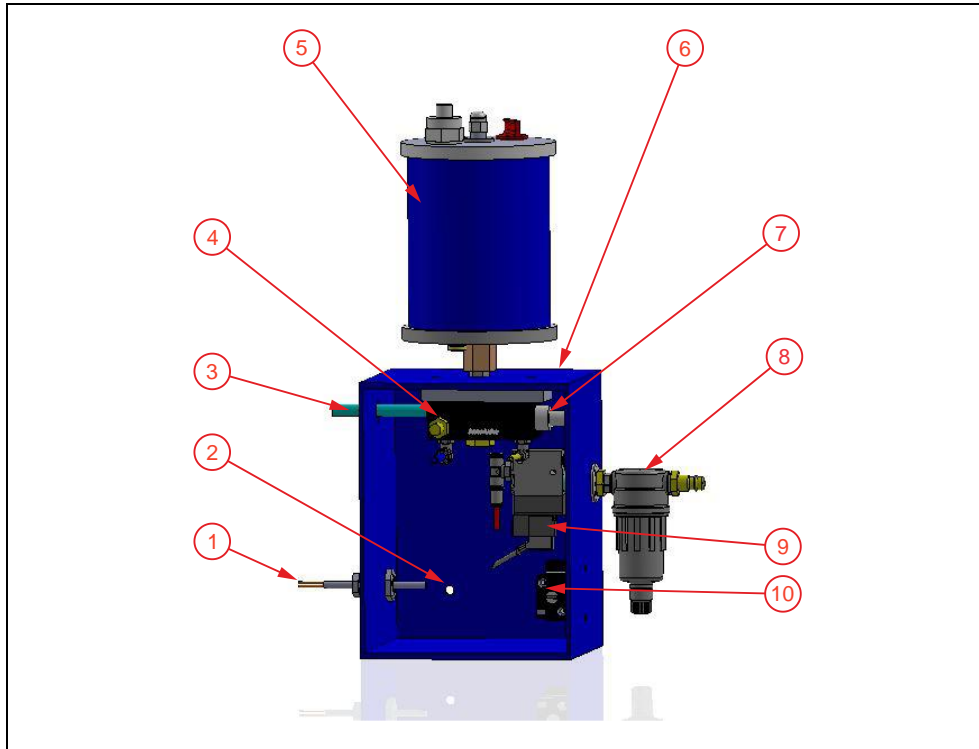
Principales componentes del aplicador equipado con bomba de aluminio
